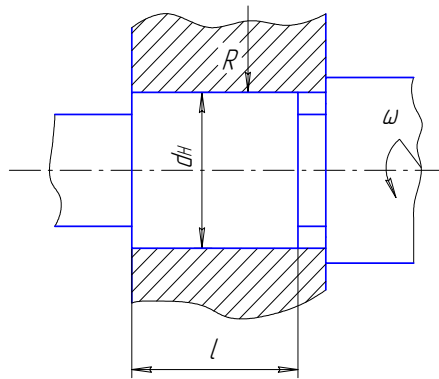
Розрахункова схема визначення допустимих зазорів
